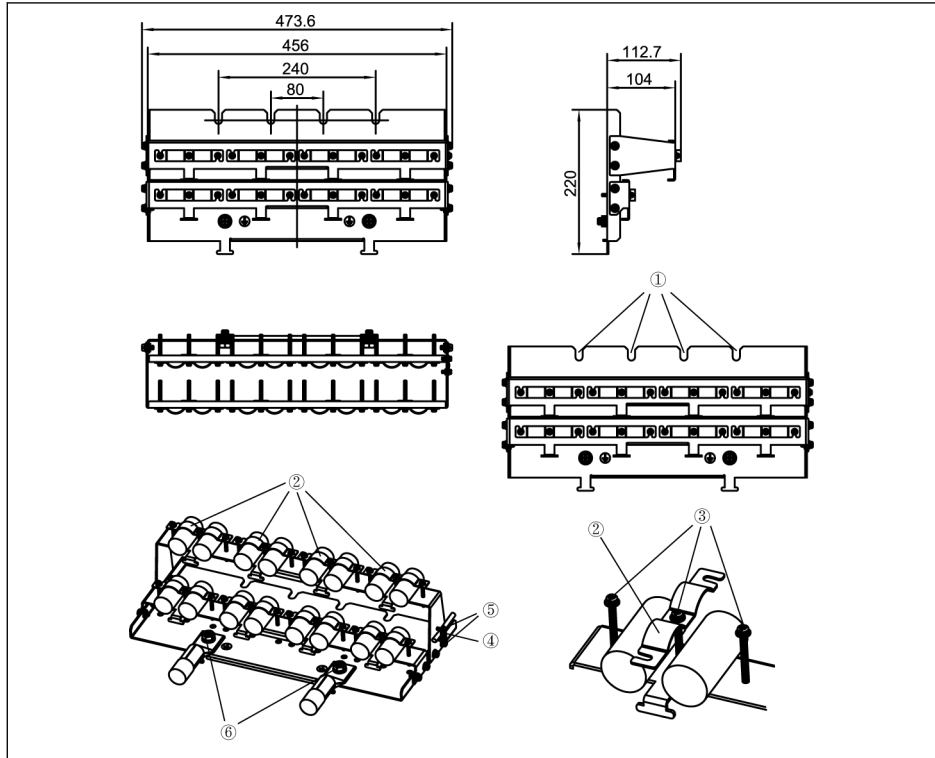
Anschluss für geschirmtes Kabel mit Zubehör für Gehäuse L (FEAM03.2-006-NN-NNNN)
